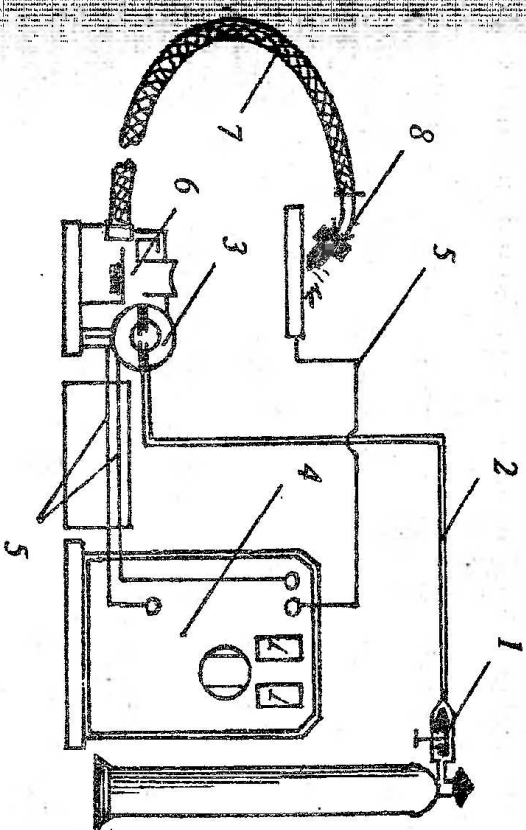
Схема полуавтомата для сварки в защитных газах.
